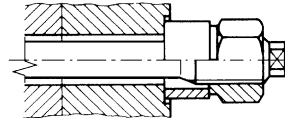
Schraubenverbindungen mit Dehnschaft (kurzes Gewinde), Sechskantmutter für Innenzentrierung und Dehnhülse (M 12 bis M 180 x 8); Dehnhülse und Sechskantmutter zentrieren die Schraubverbindung
